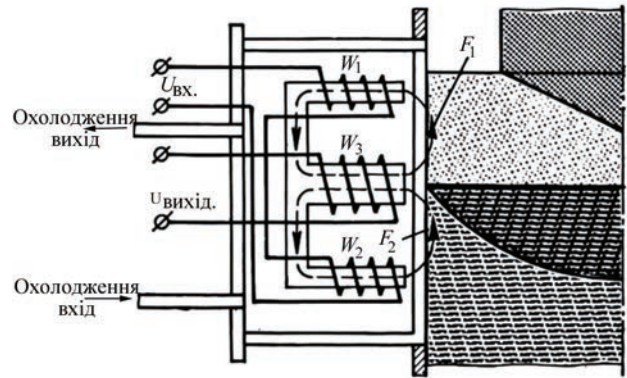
Принципова схема роботи індуктивного датчика вимірювання положення границі розділу шлак–метал: U — напруга; W — трансформатор; F — магнітний потік
